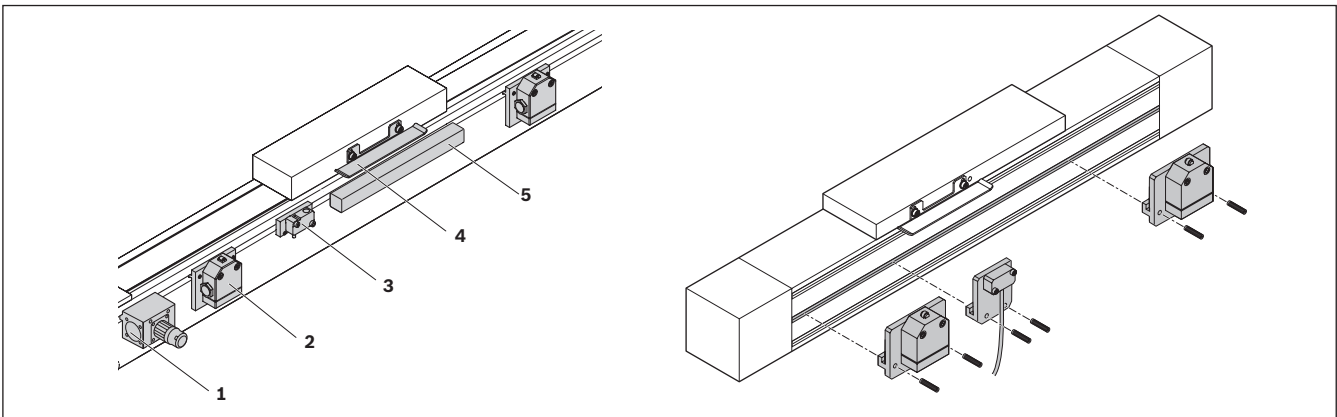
Übersicht mechanische Schalter, induktive Sensoren, Dose-Stecker, Kabelkanal, Schaltwinkel
